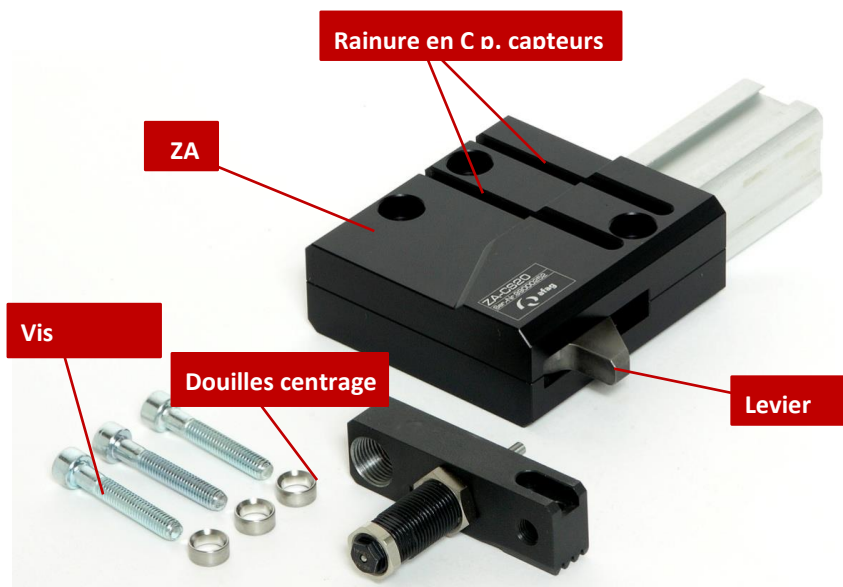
Vue d'ensemble de la butée intermédiaire ZA
